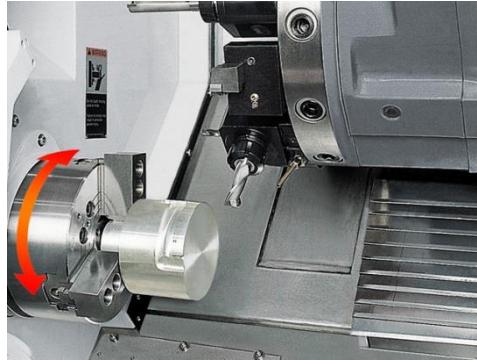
Operação de torneamento dotada de uma estação automática de ferramentas [12].
